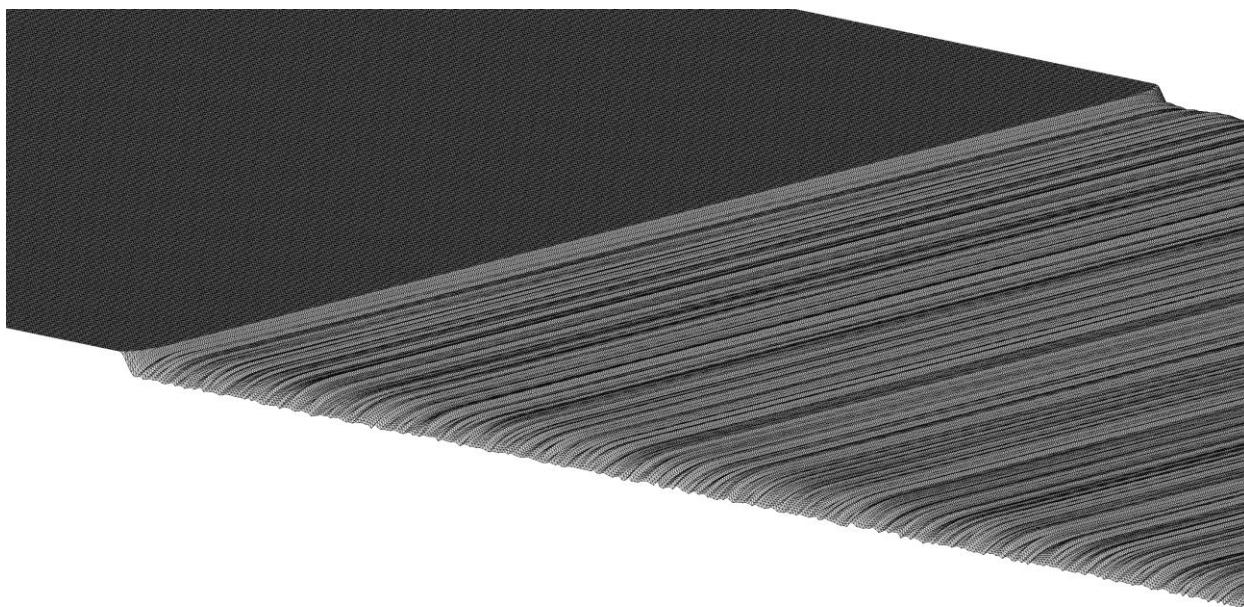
Вид поверхности детали после 3х проходов инструмента
